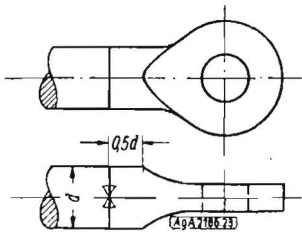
Gelenkauge mit geschmiedetem oder Stahlgußteil. Für Stumpfschweißung (Abbremschweißung) besonders geeignet
